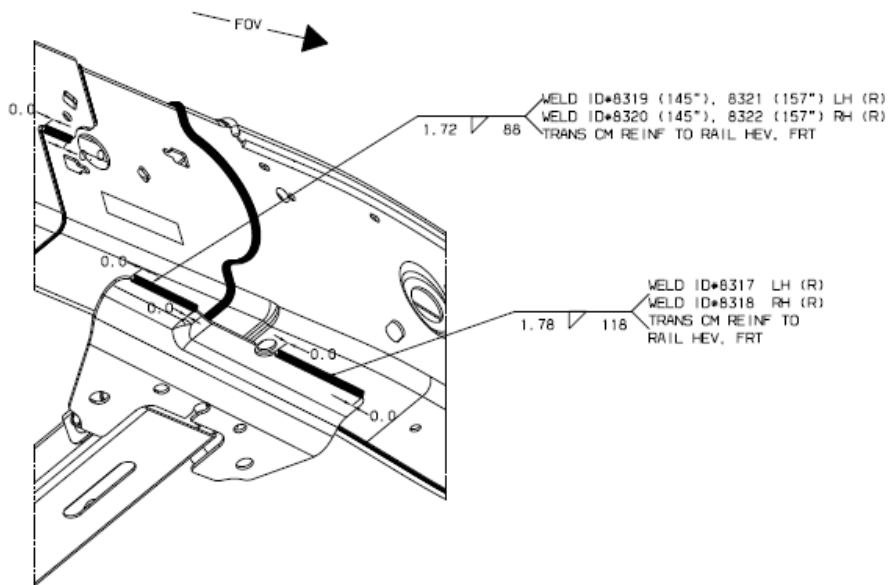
Sección 4, Información de Soldadura. [27]
